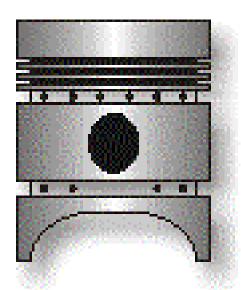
PISTÓN DE FALDÓN DE ZAPATA
